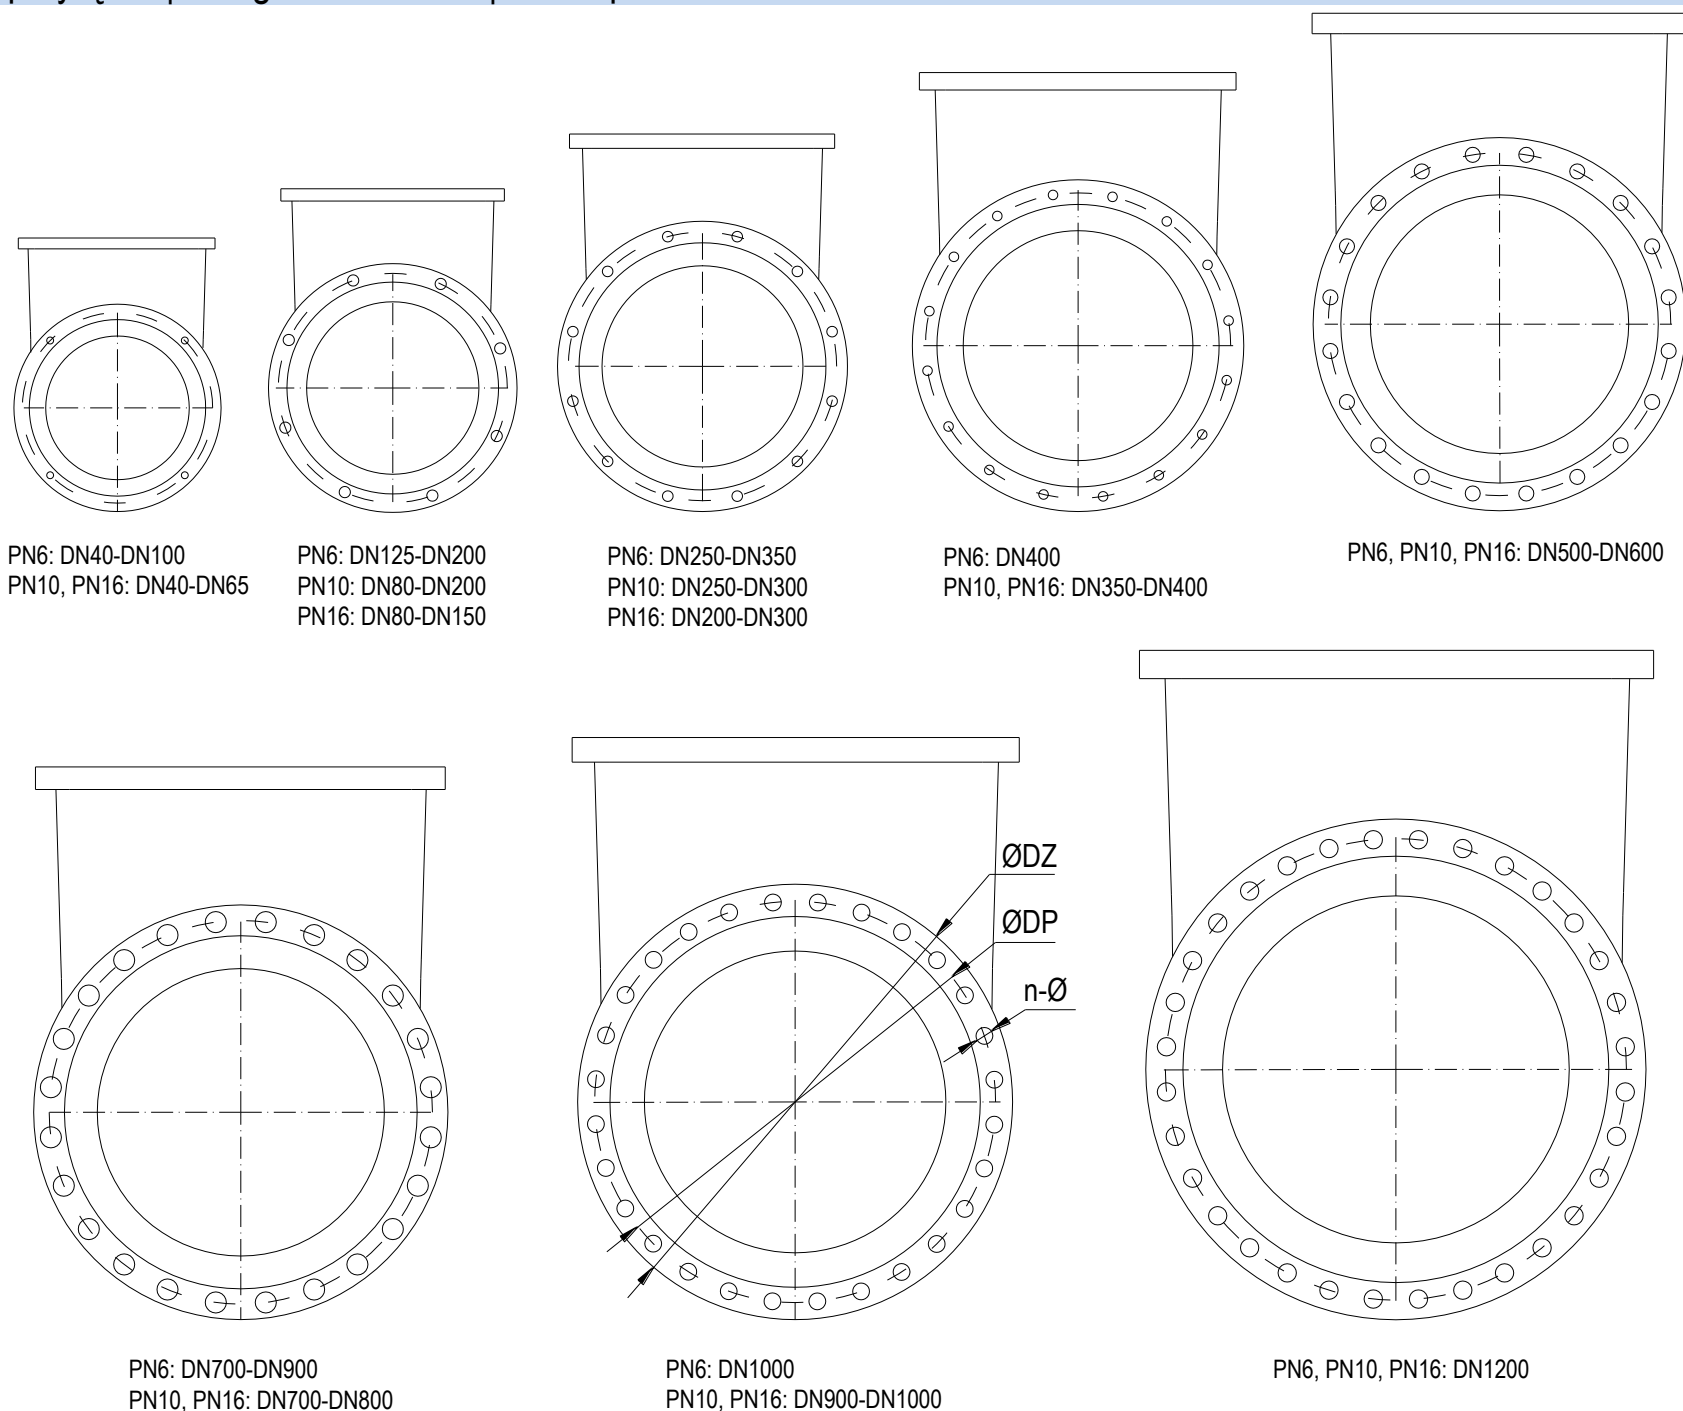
Główne wymiary urządzenia | Main device dimensions | Основные размеры устройства
